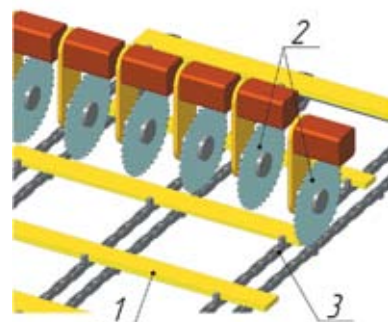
Вариант компоновки торцовочного комплекса ATK-N: 1 – пиломатериал; 2 – торцовочные пилы; 3 – цепной транспортер
